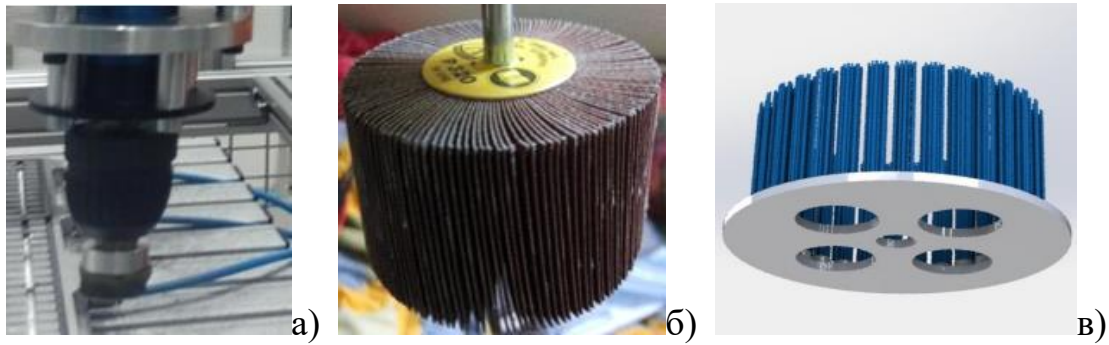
Інструменти, що використовуються для чистової обробки: обертовий (пластинчастий) інструмент (а); радіальний інструмент (б); щітка (в)
